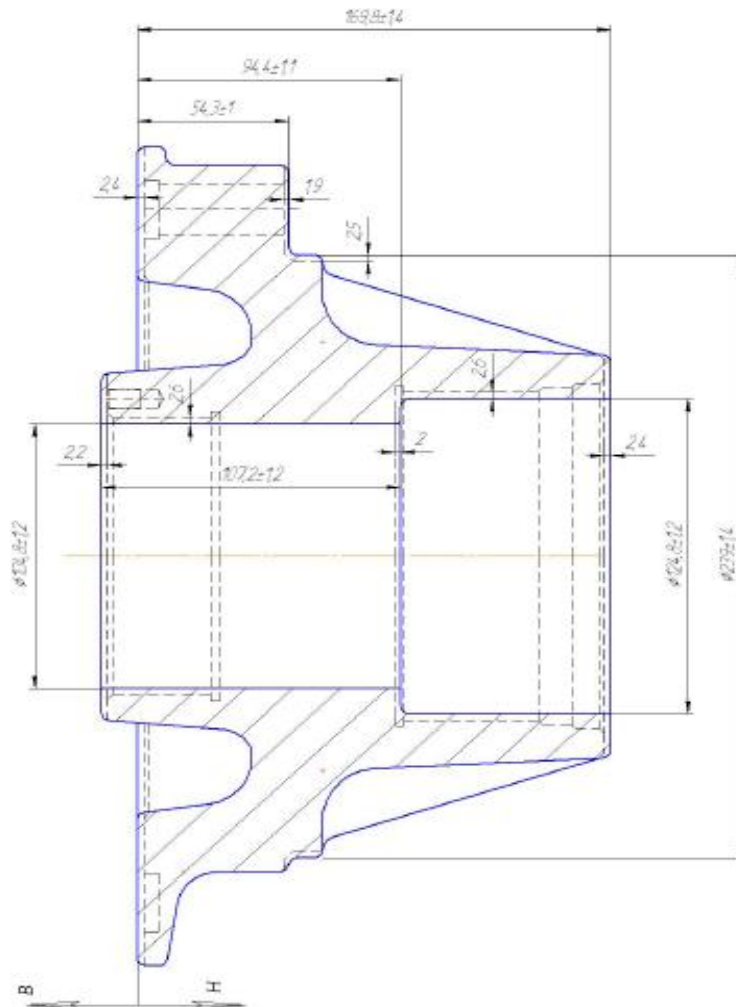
Эскиз заготовки ступицы колеса
